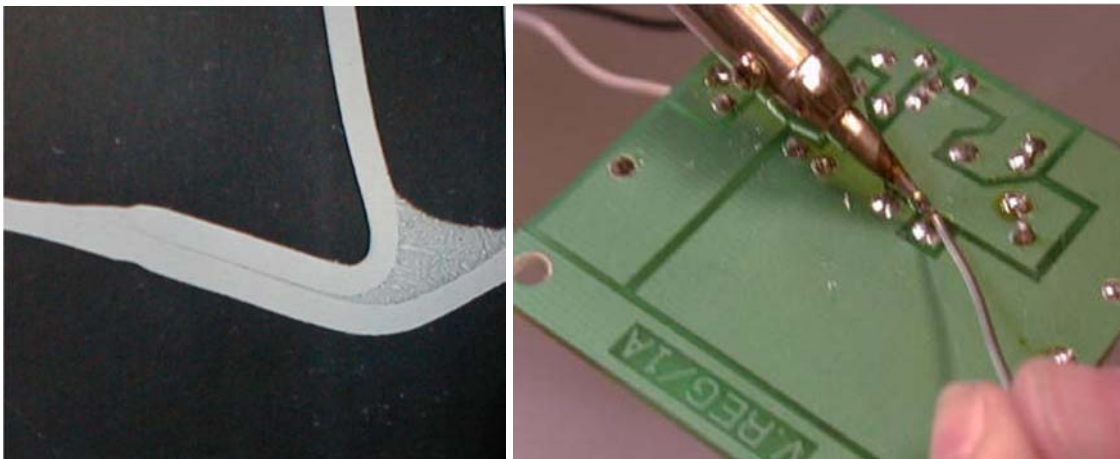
Brazagem de uma junta (esquerda) e Solda fraca de componentes eletrônicos (direita) [30]
